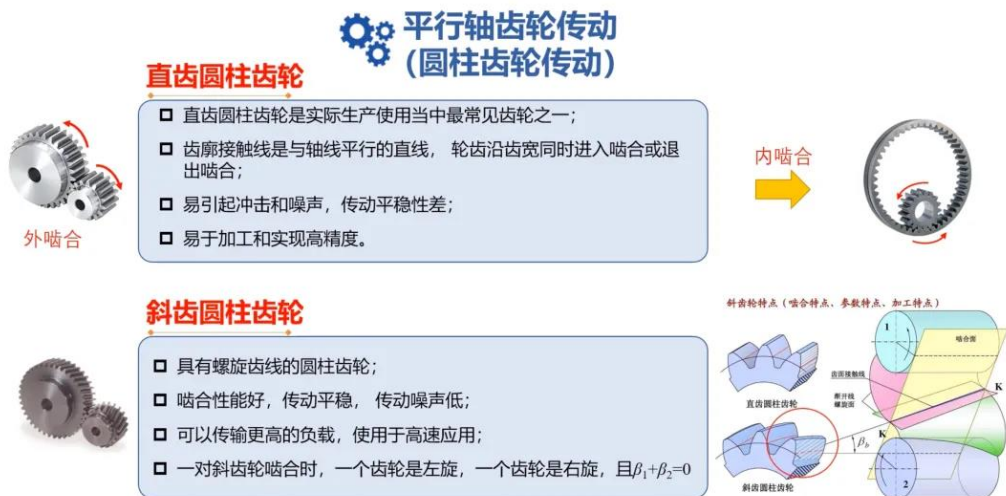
直齿圆柱齿轮和斜齿圆柱齿轮
